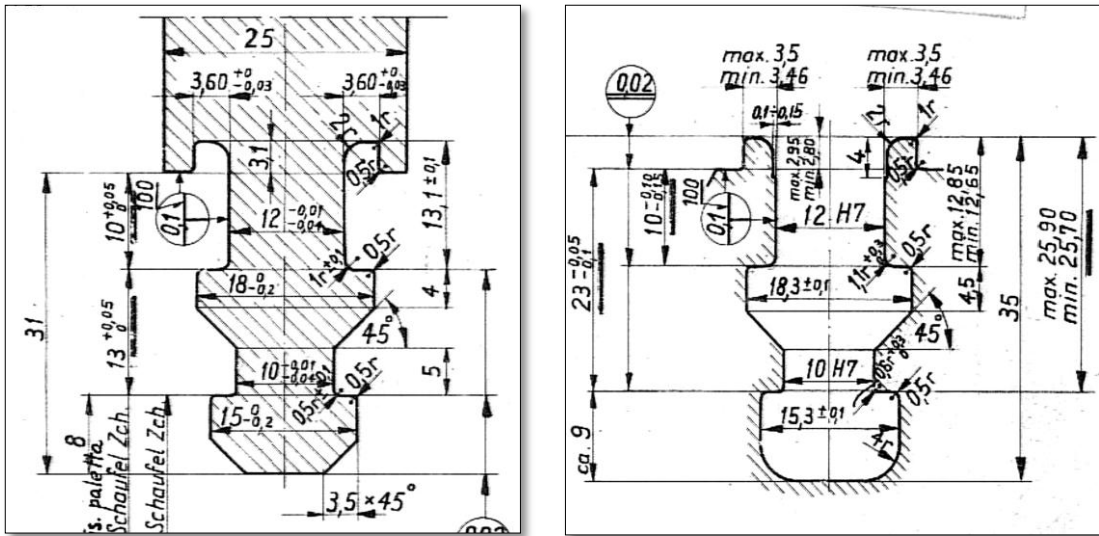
dimensioni del piede palare e della cava sul disco del 1° stadio della turbina n° 3.
